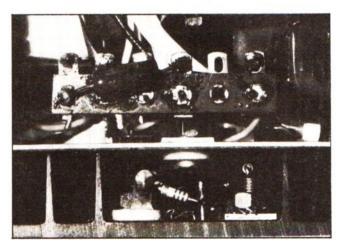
Un ensemble de deux cosses à souder, à trous de 3 mm, une ayant été coupée assez court, soudée sur l'autre que l'on a pliée, constitue une « équerre » simplifiée pour la fixation du circuit imprimé.
